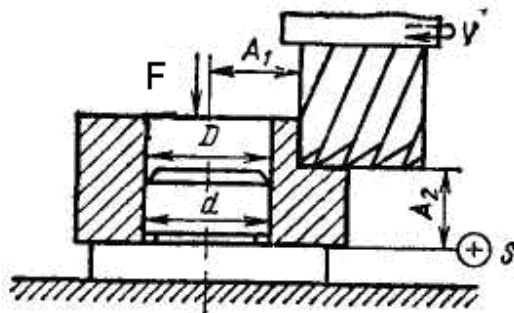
Схема фрезерування втулки (до задачі 1.29.)
